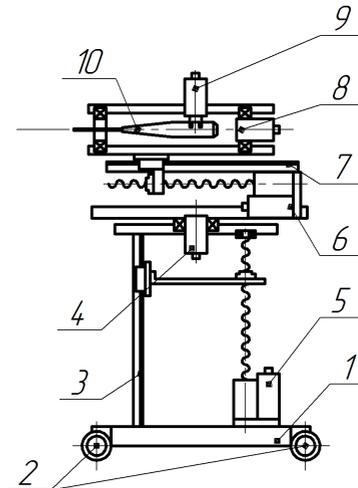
Конструкция робота-ассистента: 1 – стойка; 2 – колесные опоры; 3 – линейная направляющая с кареткой; 4- поворотный электропривод стойки; 5 – линейный электропривод стойки; 6 – линейный привод манипулятора; 7 – линейная направляющая с кареткой манипулятора; 8 – поворотный привод манипулятора; 9 – привод рукоятки уретроскопа; 10 – уретроскоп
